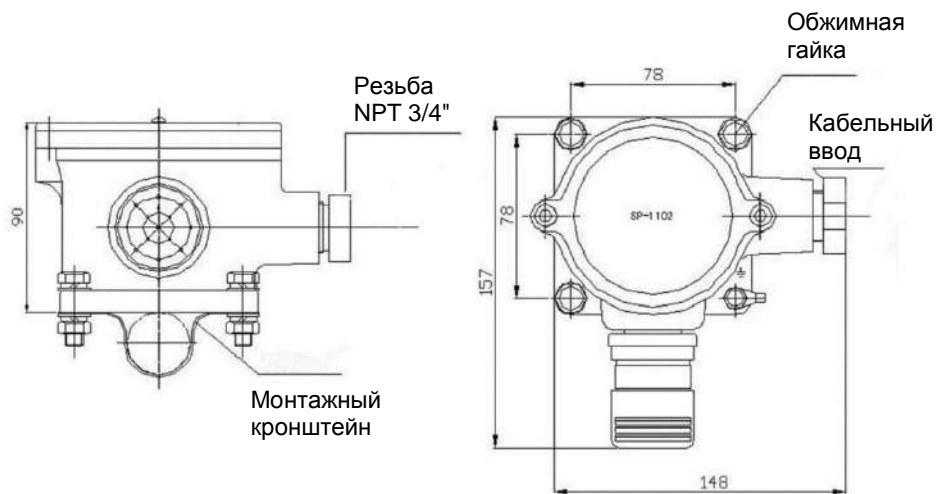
Чертеж с монтажными размерами газоанализатора
